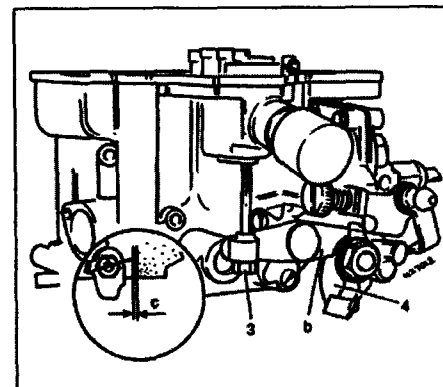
Регулировка клапана вентиляции поплавковой камеры
